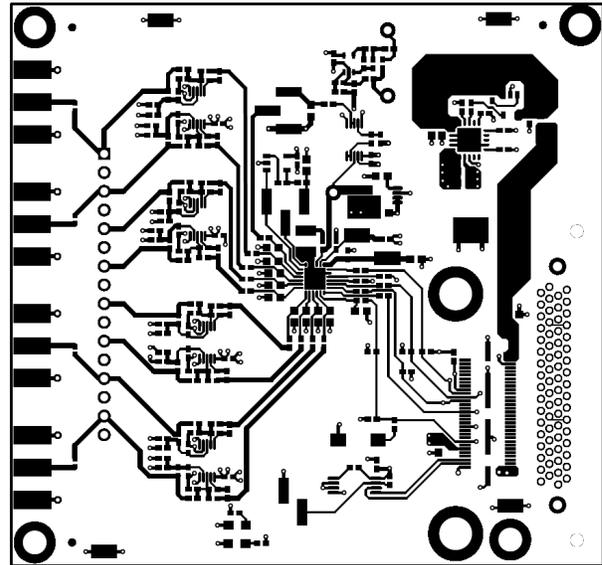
ADS8332EVMV2 PCB 第 1 层 : 顶层
